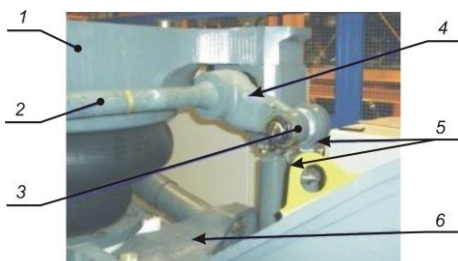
Соединение элементов стабилизатора боковой качки ВСП «Сапсан»:
